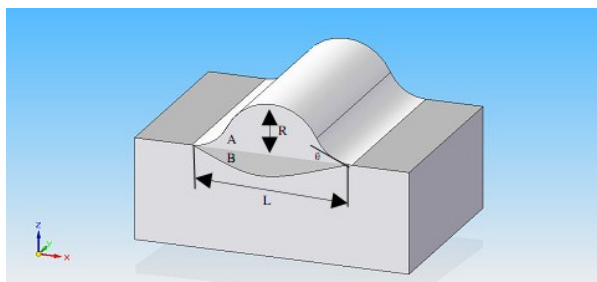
Perfil geométrico ilustrativo de um cordão soldado. R- reforço; L- largura; θ- ângulo de molhamento.
